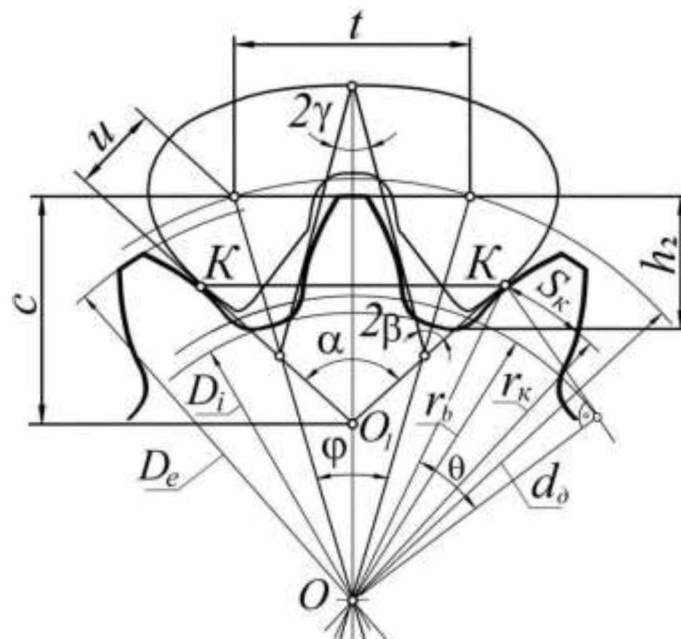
Зчеплення пластини зубчастого ланцюга із зубами евольвентної зірочки
